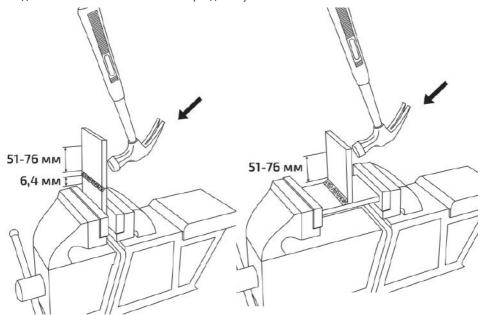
Проверка на прочность сварного соединения.
